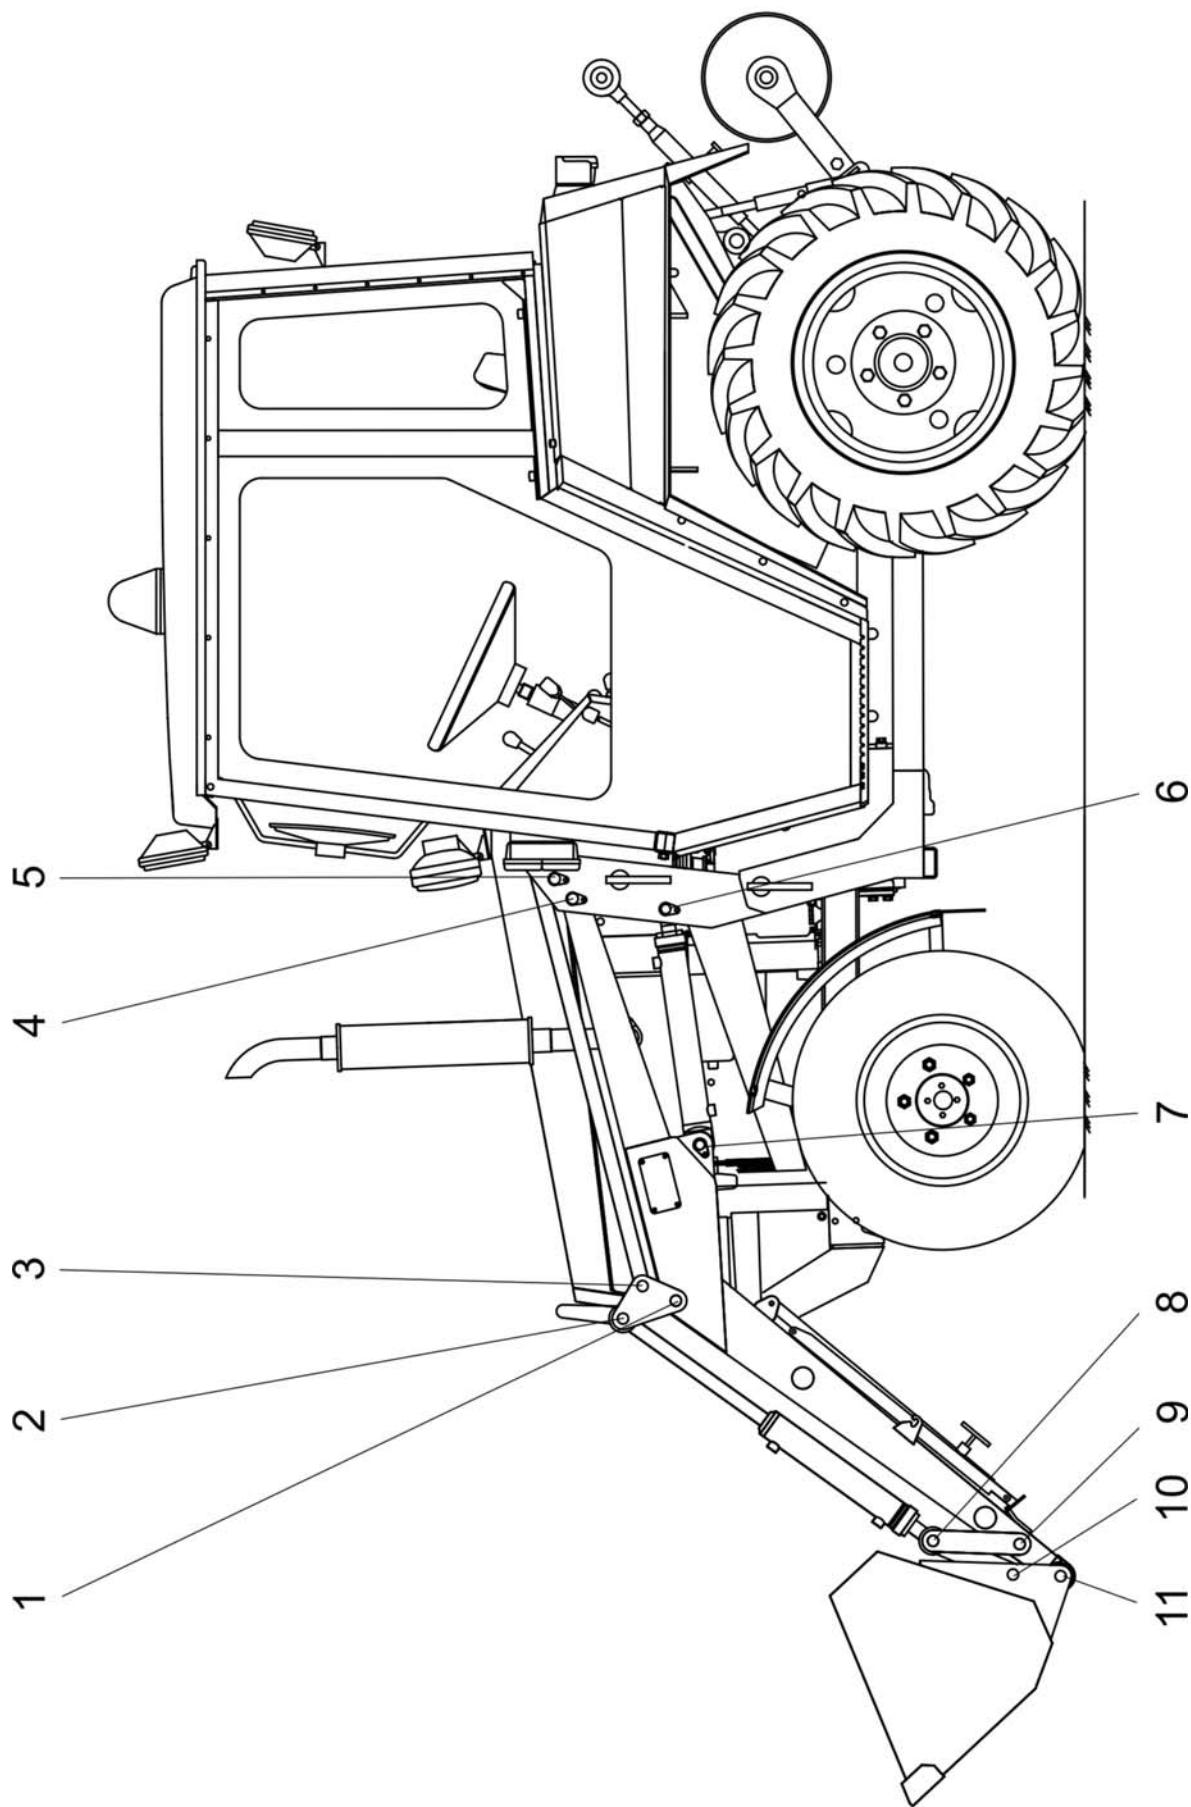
Схема смазки рабочего оборудования погрузчика
